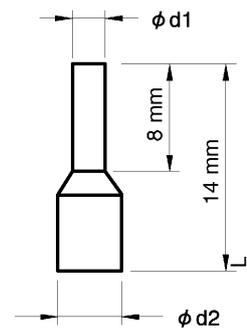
Dimensions de la borne sans soudure droite
